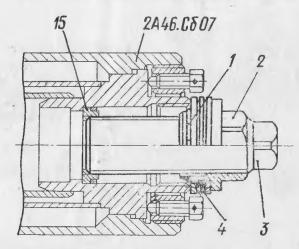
Установка прибора 2A26.C6 42-9 для вынимания кольца 2A26.07-45:
